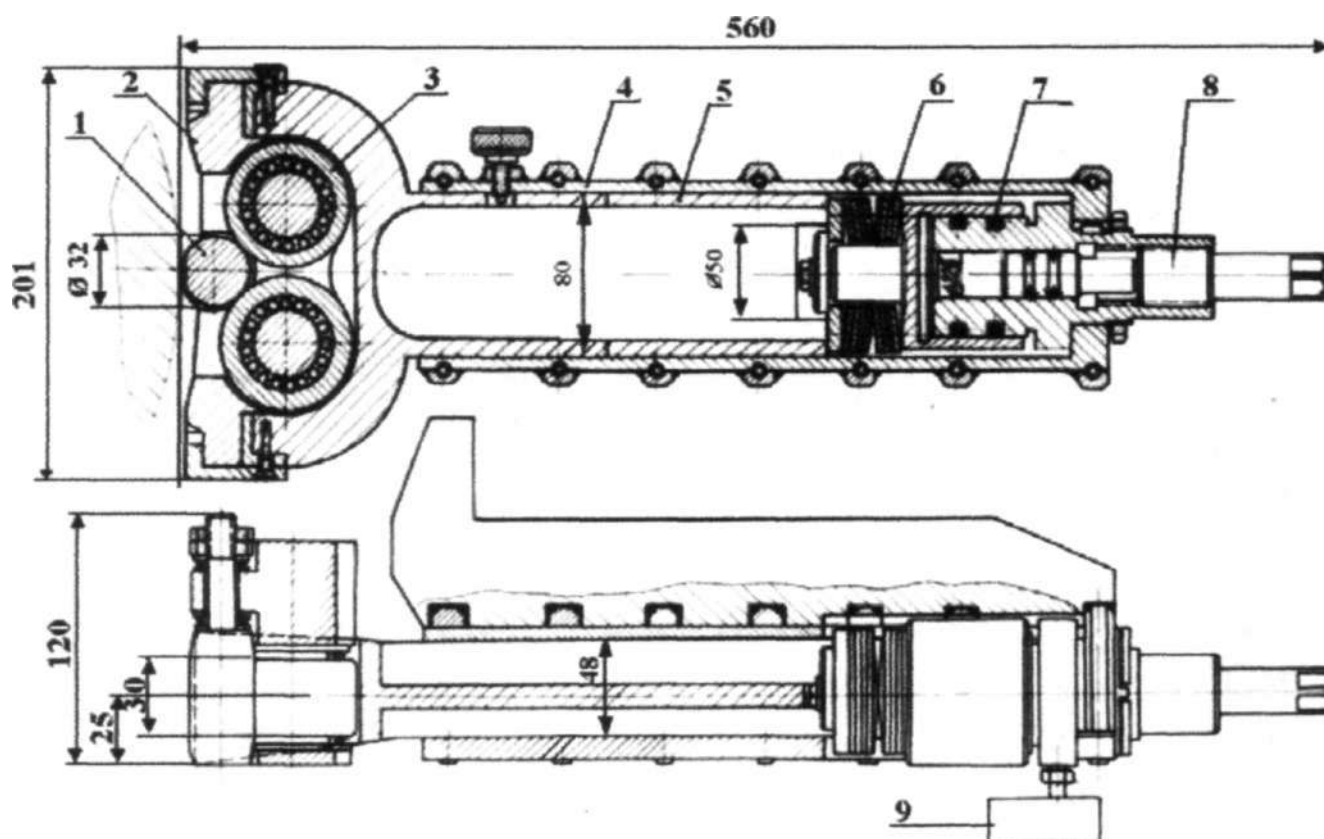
Устройство для обкатывания валов самоустанавливающимся цилиндрическим роликом диаметром 32 мм
